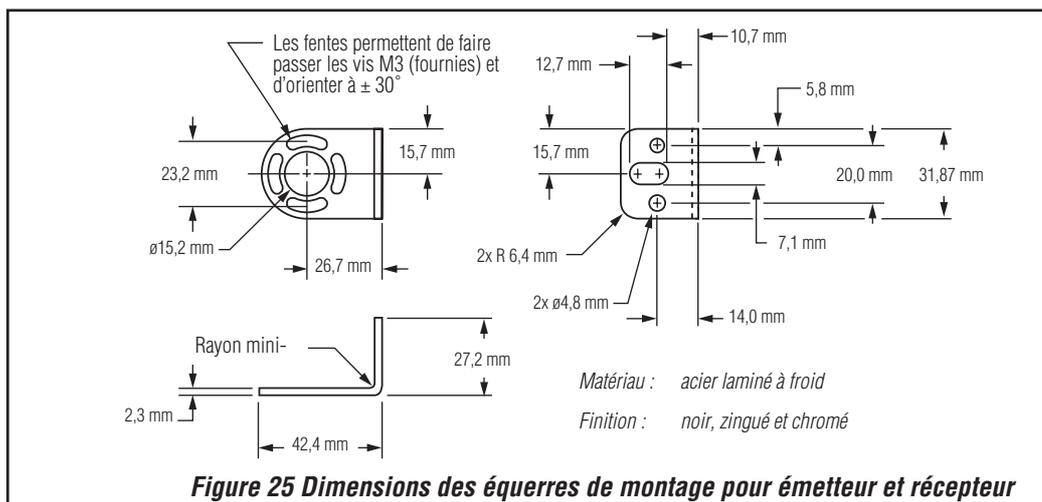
Dimensions des équerres de montage pour émetteur et récepteur
